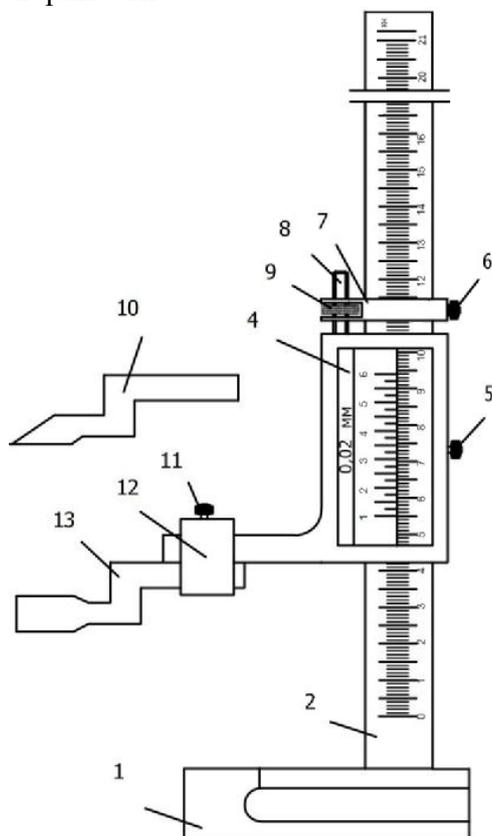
Штангенрейсмас ШПР: 1 – основание; 2 – штанга с основной измерительной шкалой; 3 – подвижная рамка; 4 – шкала нониуса; 5, 6 – стопорный винт; 7 – хомут; 8 – винт микрометрический; 9 – гайка микрометрического винта.
